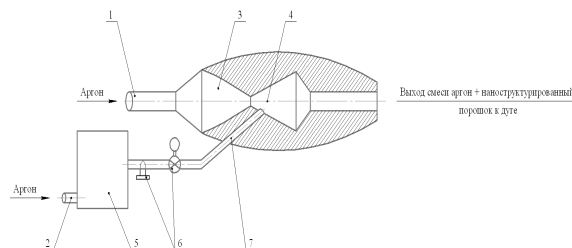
Схема устройства подачи нанопорошка в зону сварки:
